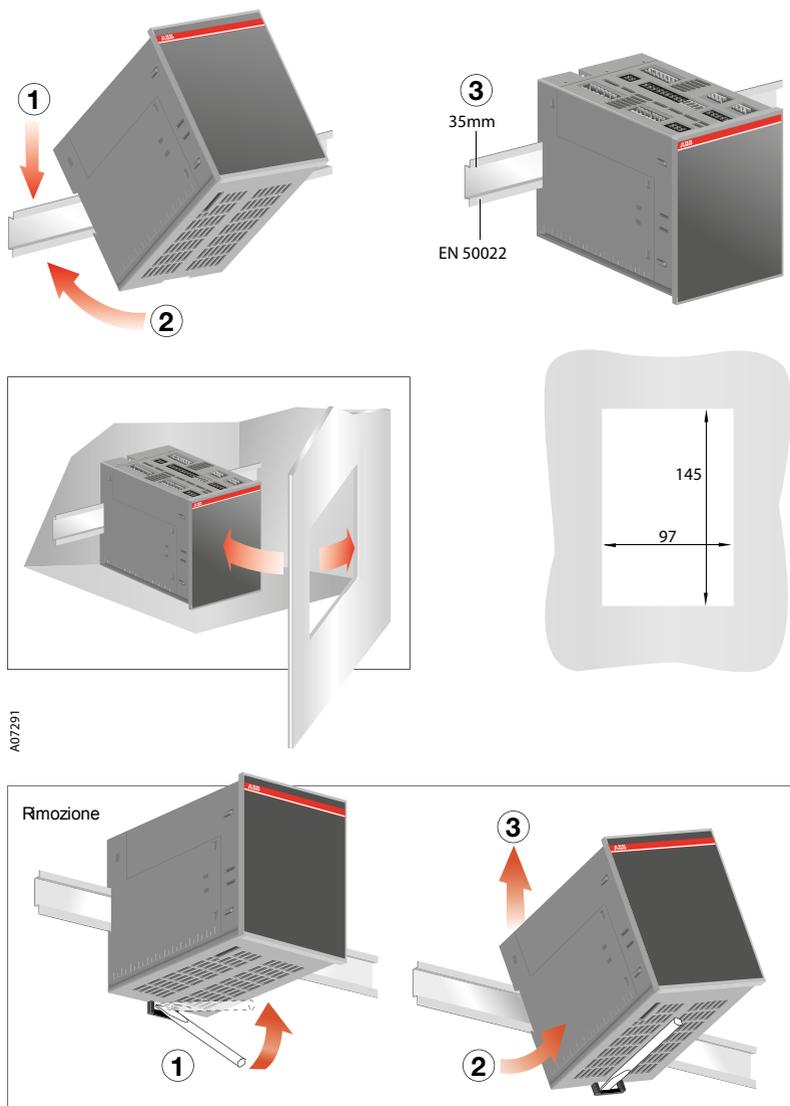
Unità di controllo automatica OMD800, montaggio su guida DIN, perforazione della portella
